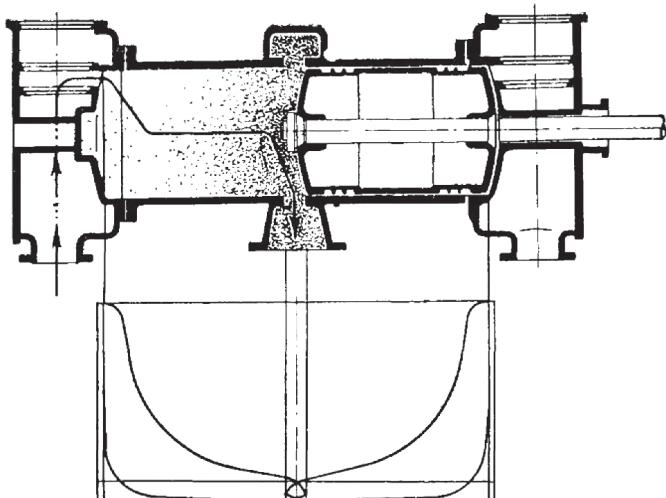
Схематический разрез через цилиндр прямоточной паровой машины.
